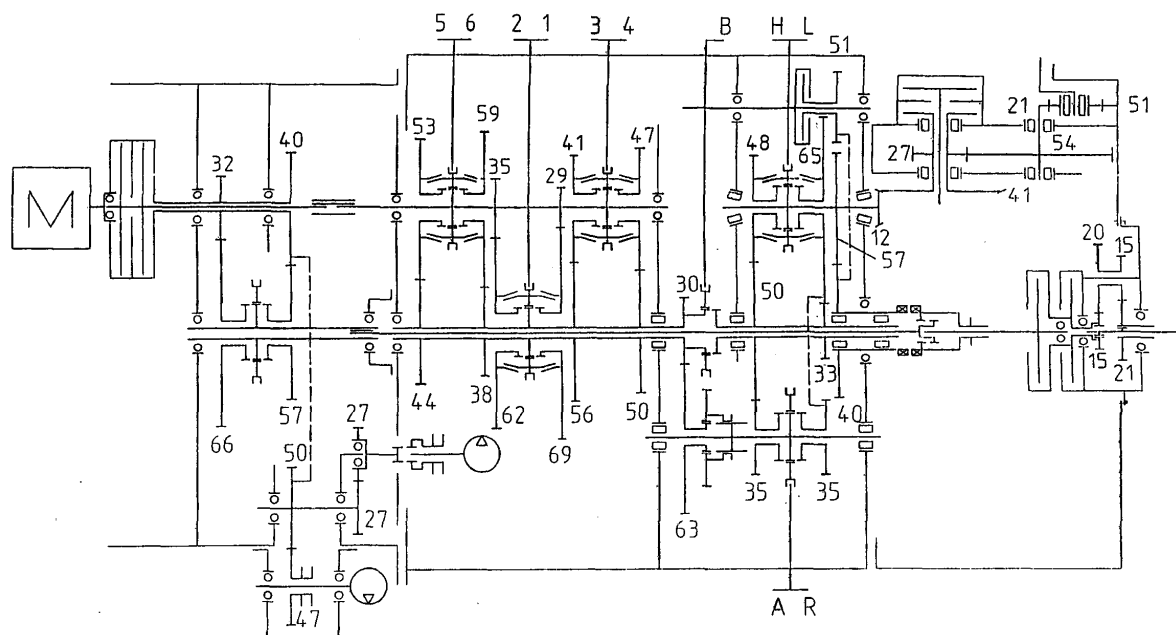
Кинематическая схема опытной коробки передач с двухпарным зацеплением
